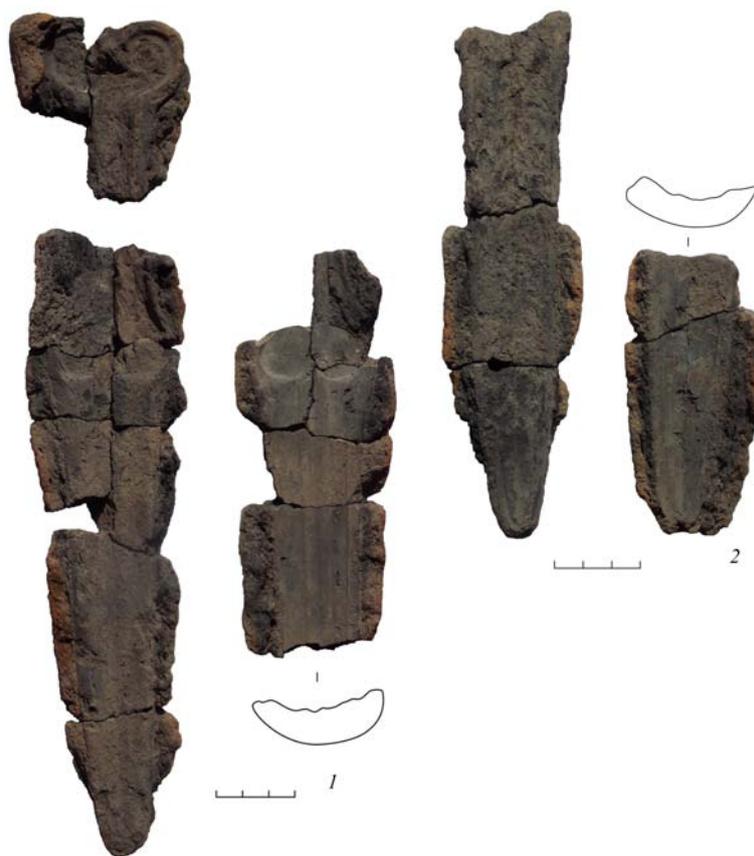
Металлопроизводственный комплекс ямы № 23 сооружения 2: створки двух форм для отливки кинжалов.
